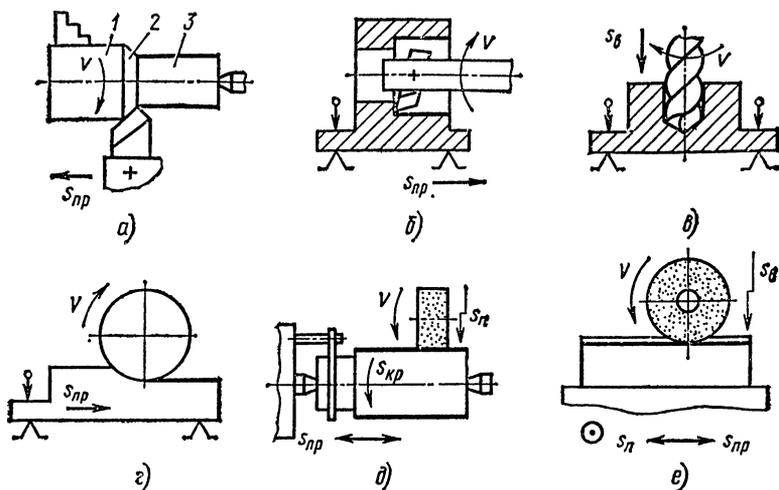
Элементы схем обработки и схемы обработки заготовок точением (а), растачиванием (б), сверлением (в), фрезерованием (г), шлифованием на кругло- (д) и плоскошлифовальных станках (е)
